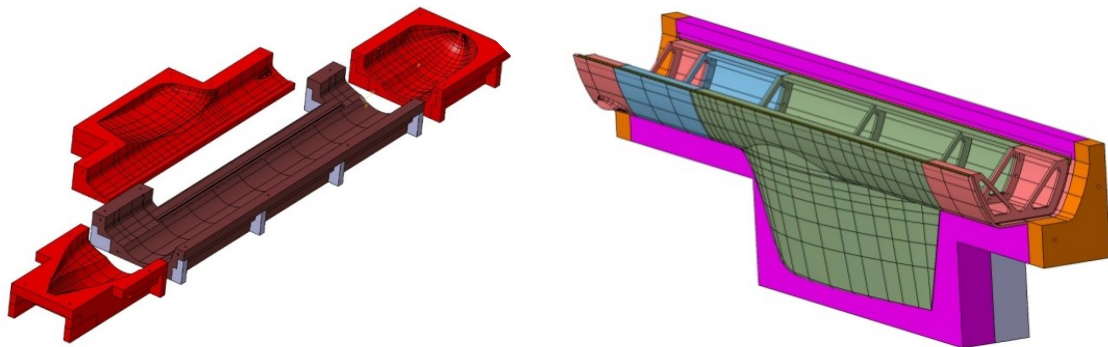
Laminierwerkzeuge für die Bauteile der Außenhülle
